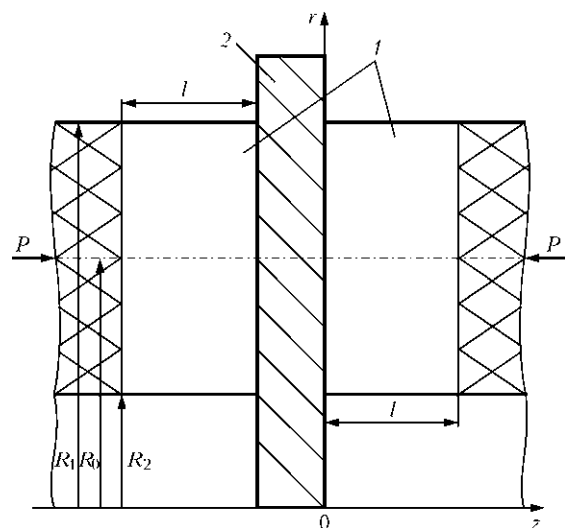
Расчетная схема процесса сварки полиэтиленовых труб: 1 — исходные заготовки; 2 — нагревательный инструмент
